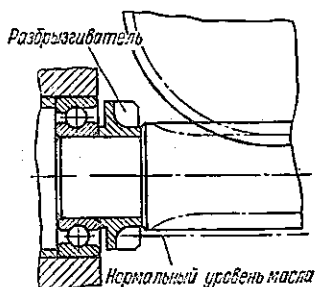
Смазывание червячной передачи с помощью разбрызгивателя
